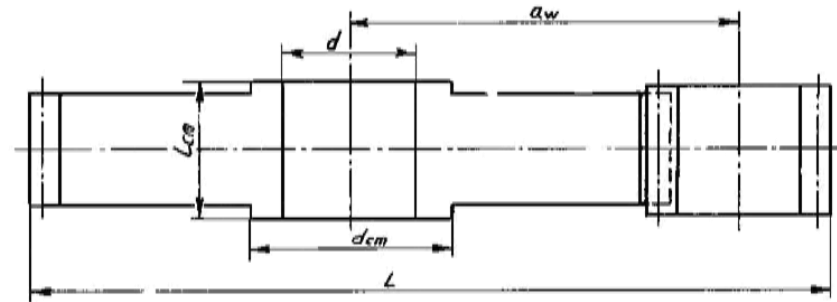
Последовательность разработки чертежа общего вида цилиндрического одноступенчатого редуктора
